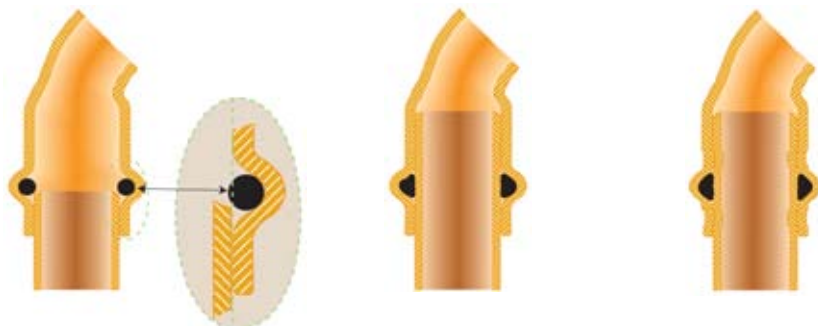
Detalles de diseño y montaje del accesorio de presión
